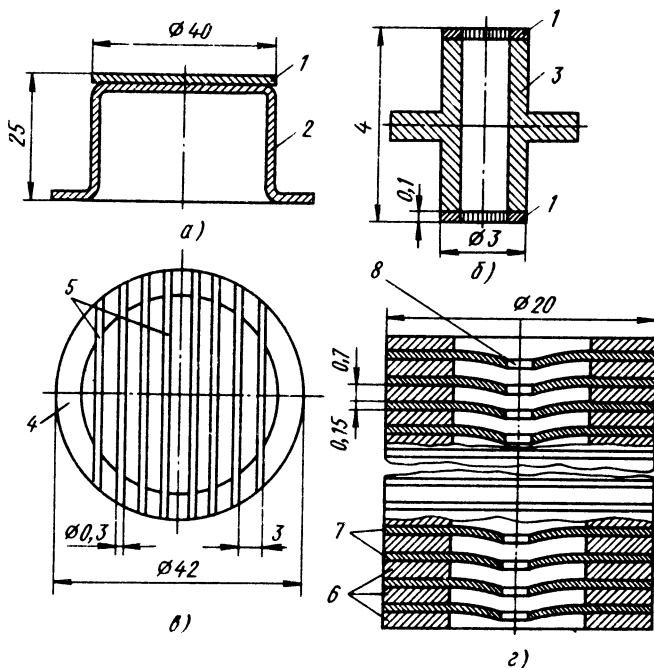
Элементы приборов, изготавливаемые диффузионной сваркой:
